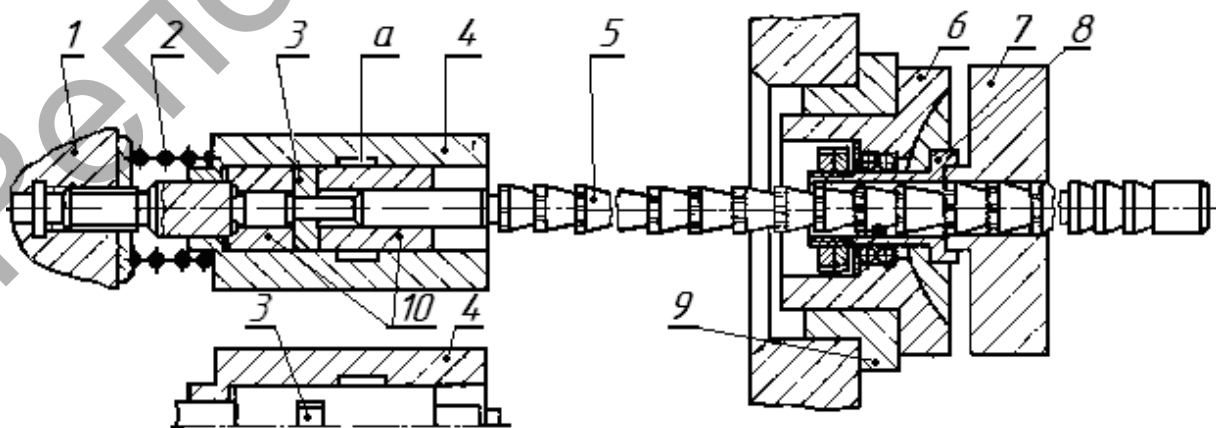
Схема крепления инструмента и детали на протяжной операции
